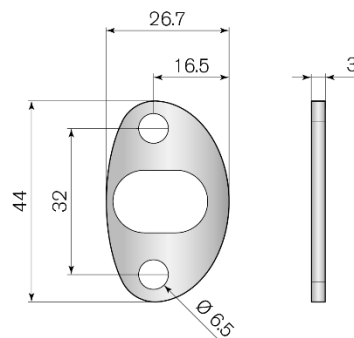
Maße des GAT SMART.Lock 70x1 (Maße in mm)
